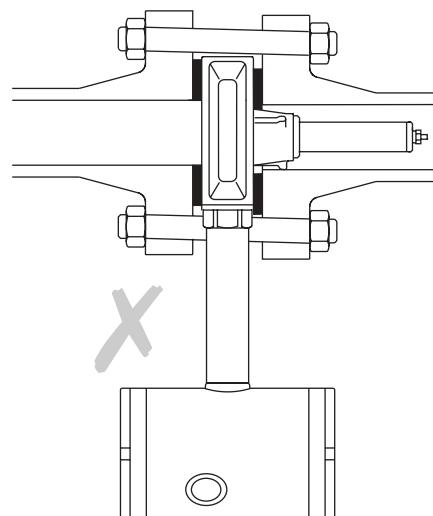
Установка прокладок и центровка трубы проведены неправильно
